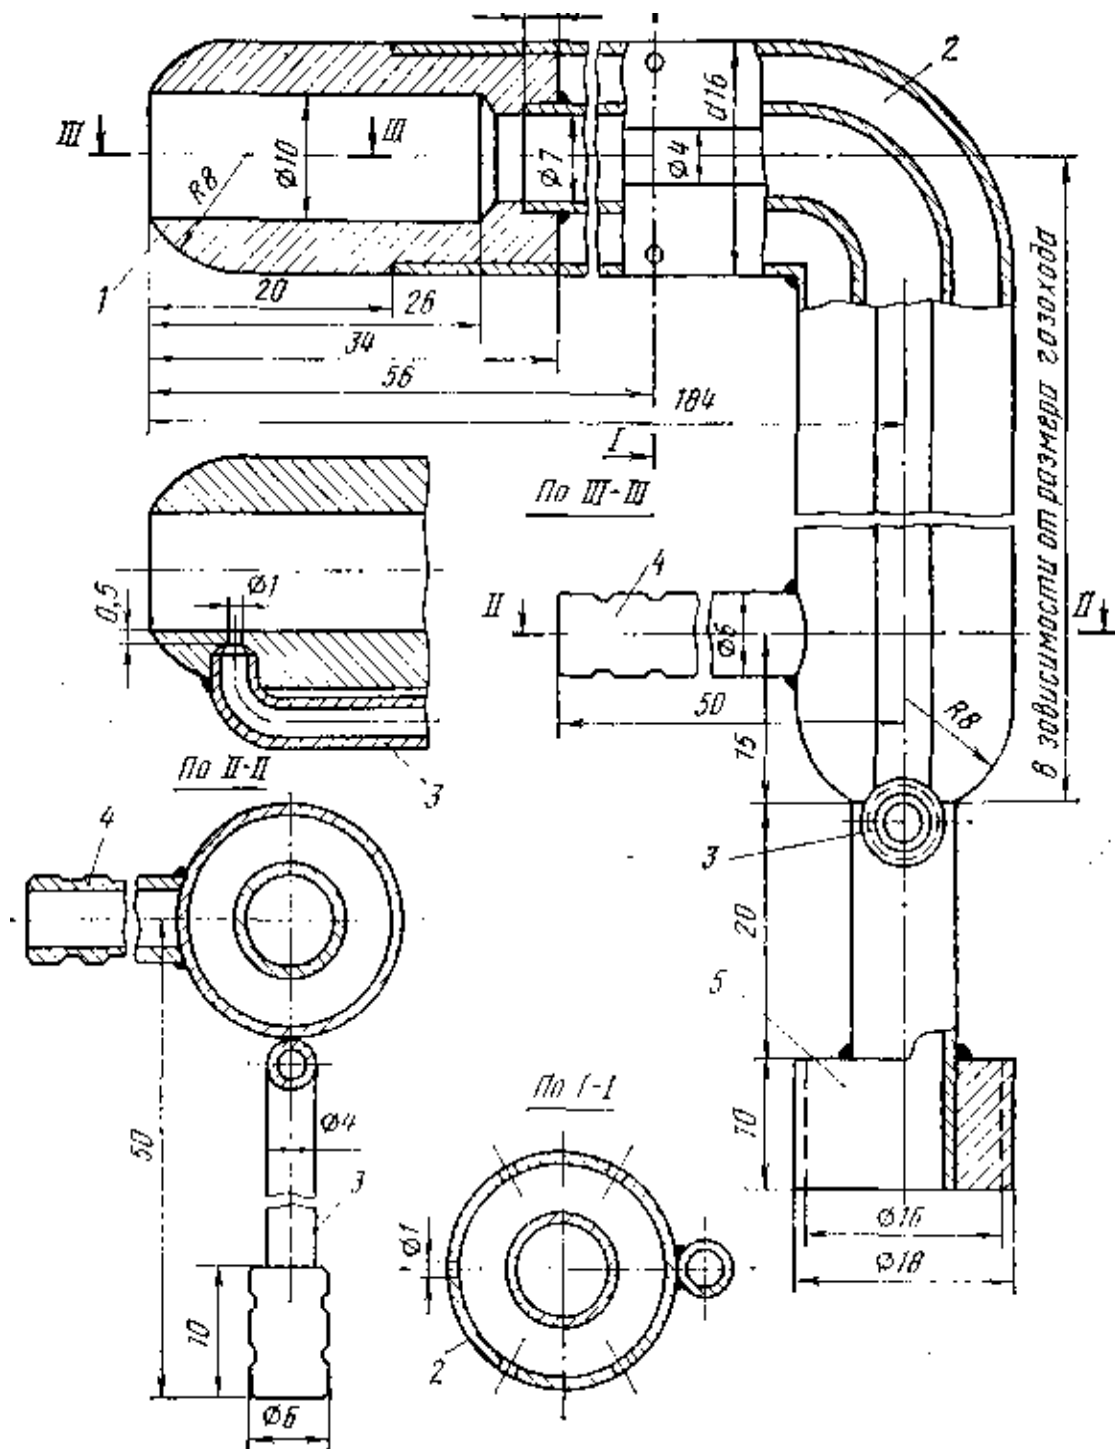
Заборная трубка нулевого типа конструкции ОАО «ВТИ»:
